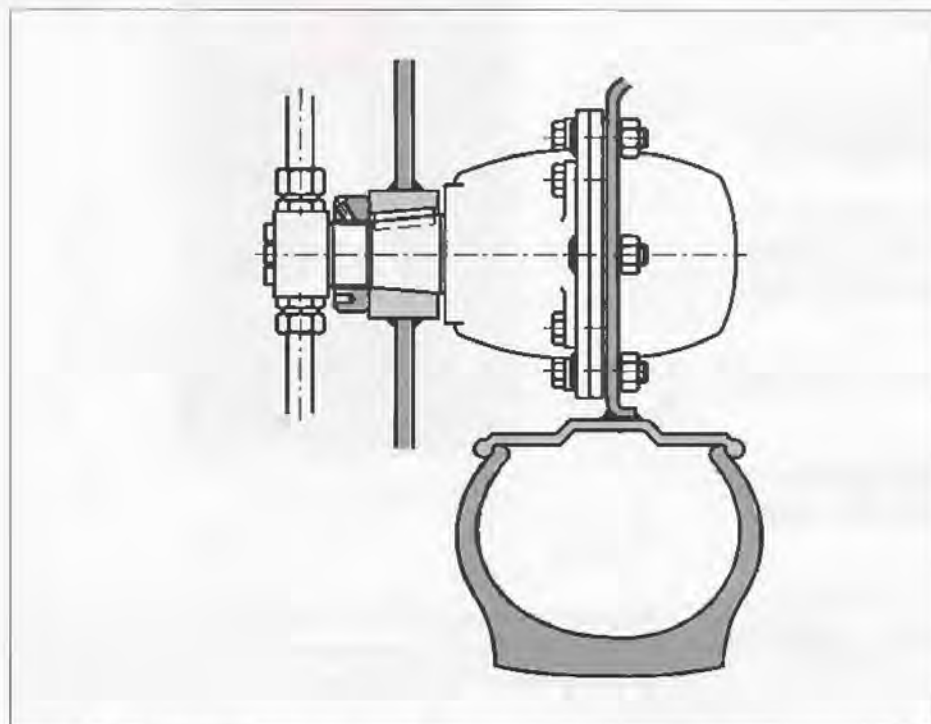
Аксиально-поршневой гидромотор с вращающимся корпусом в роли колесного привода
